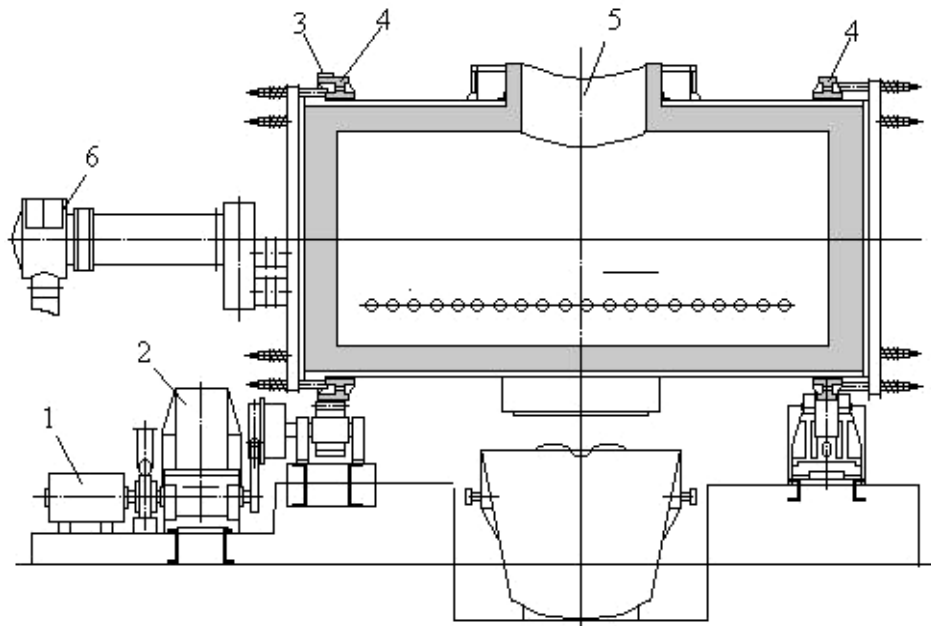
Схема горизонтального конвертера: 1 – электродвигатель; 2 – редуктор; 3 – зубчатый венец; 4 – опорные бандажи; 5 – горловина; 6 – сальниковое устройство
